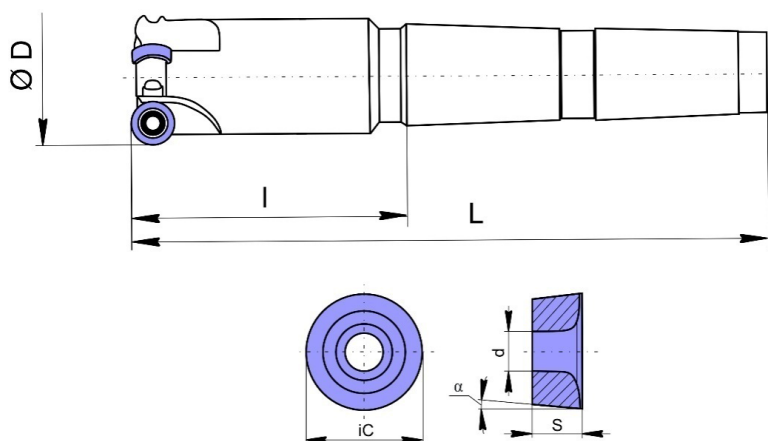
Схема и геометрические параметры фрезы и сменной режущей пластины
